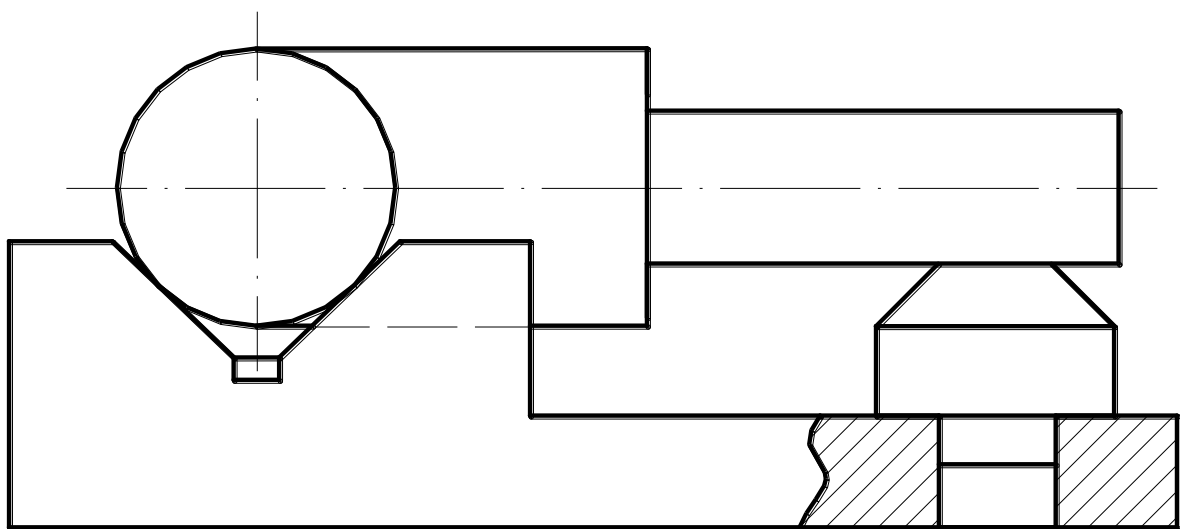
Схема встановлення заготовки в призмі з нерухомою опорою
